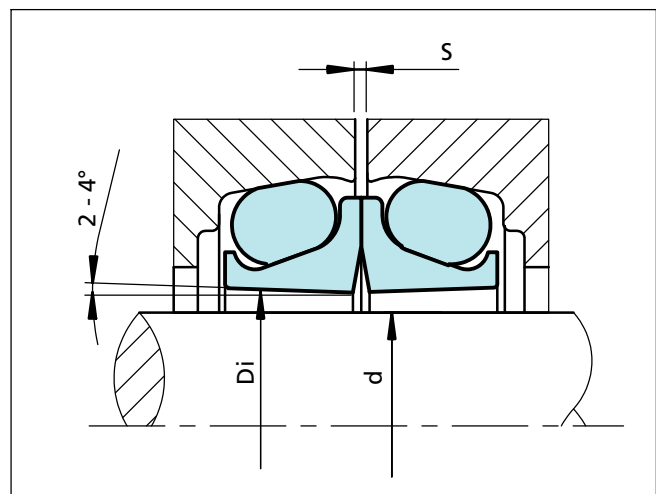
Gussausführung mit formbedingter Schräge am Innendurchmesser
